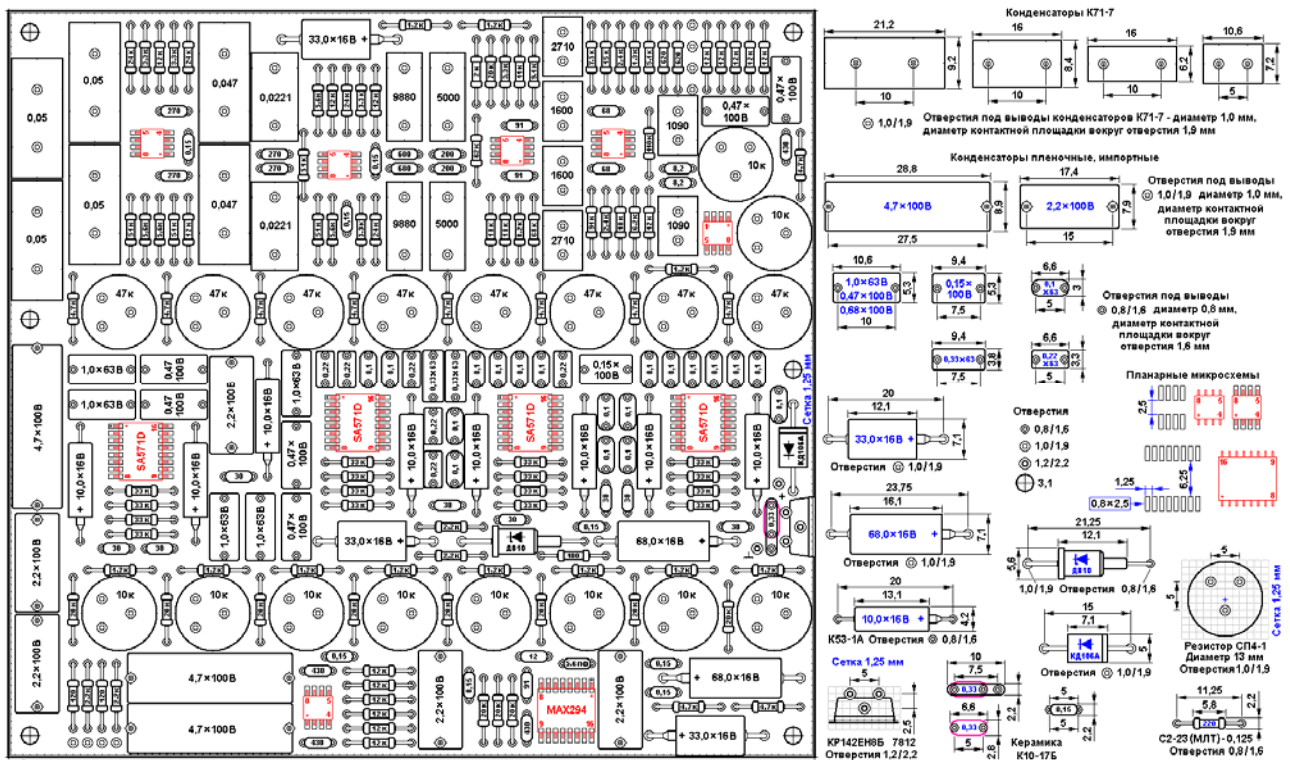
Расположение деталей на печатной плате, установочные размеры и формовка выводов
